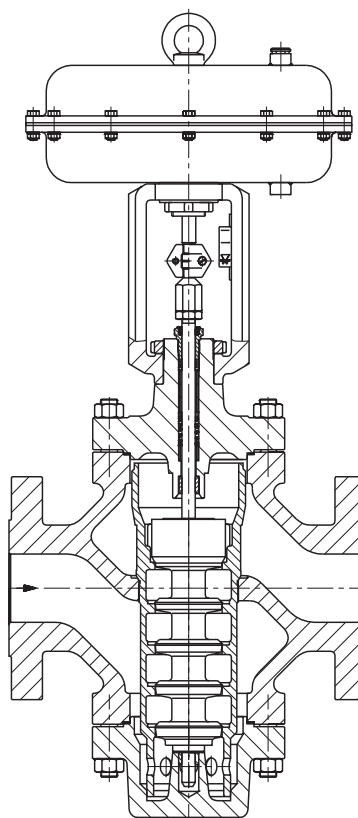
· Регулирующий клапан типа 255-1 с пятиступенчатым аксиальным конусом
